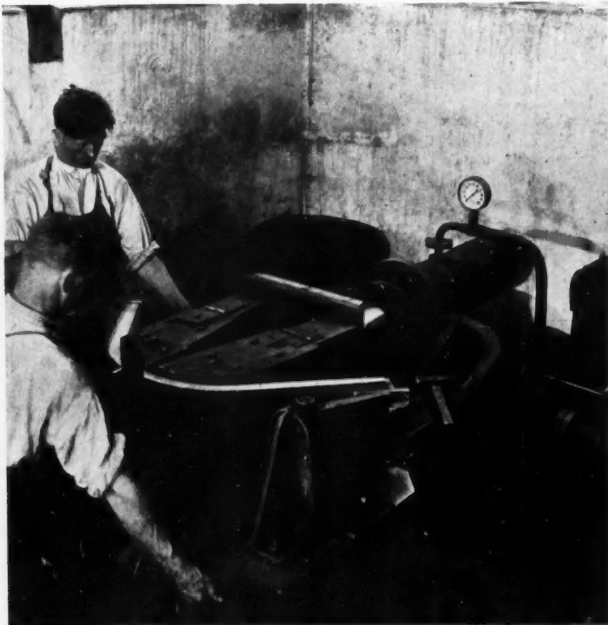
MACHINE A COURBER HYDRAULIQUE: LA PIÈCE EST PRISE ENTRE LA FORME ET UNE LAME D'ACIER EXTÉRIEURE
